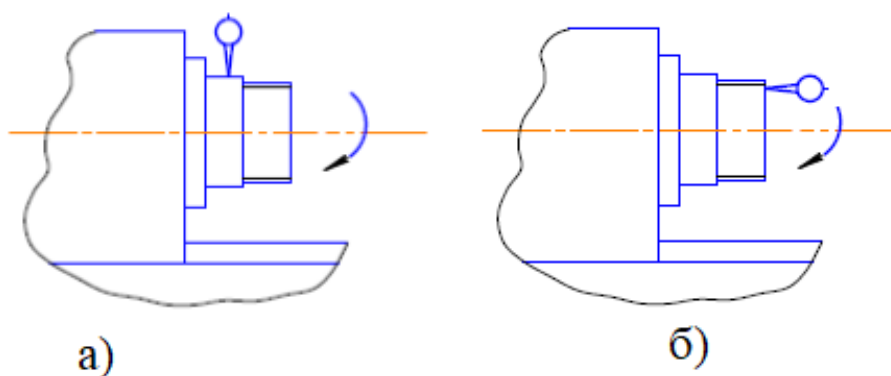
Схема установки индикатора часового типа для проверки биения центрирующей шейки шпинделя: а) радиального и б) осевого биения
